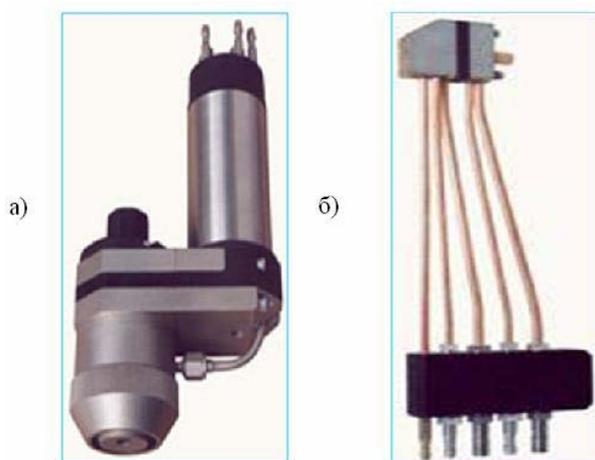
Плазмтроны для плазменно-порошкового напыления:
